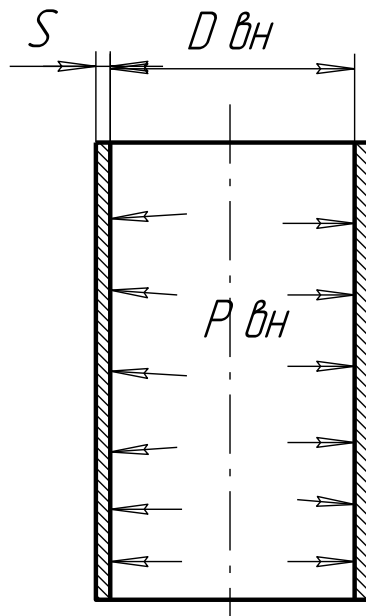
Розрахункова схема циліндричної обичайки
